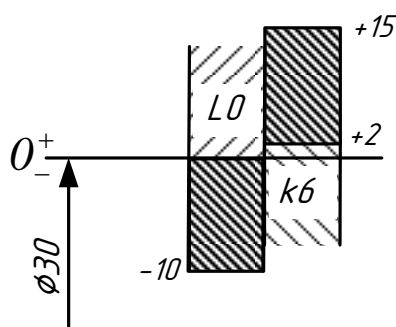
Схема полей посадки внутреннего кольца подшипника с валом
